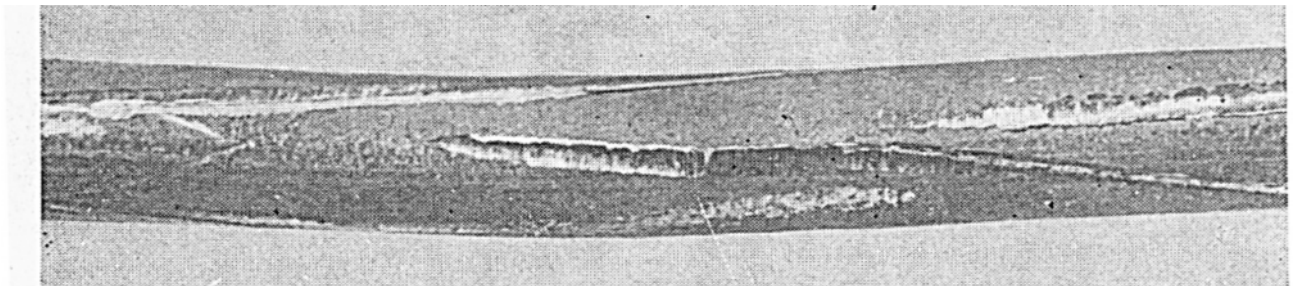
Пруток с повреждением поверхности, полученным при плавке.
